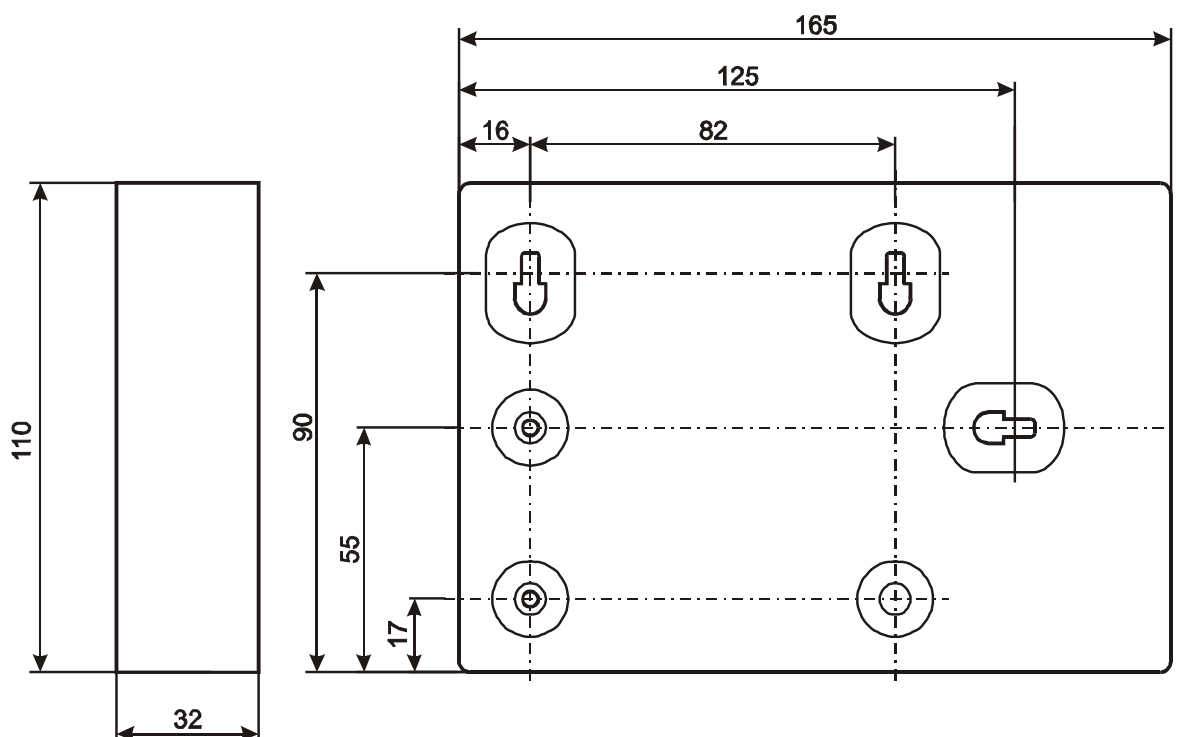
Габаритные и присоединительные размеры корпуса ТИ
